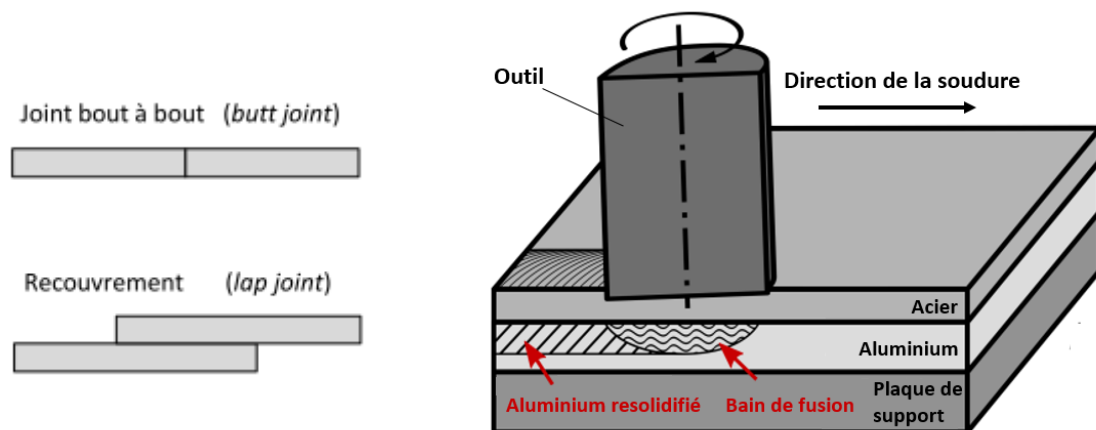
Gauche : illustration des configurations de joint de soudure.
